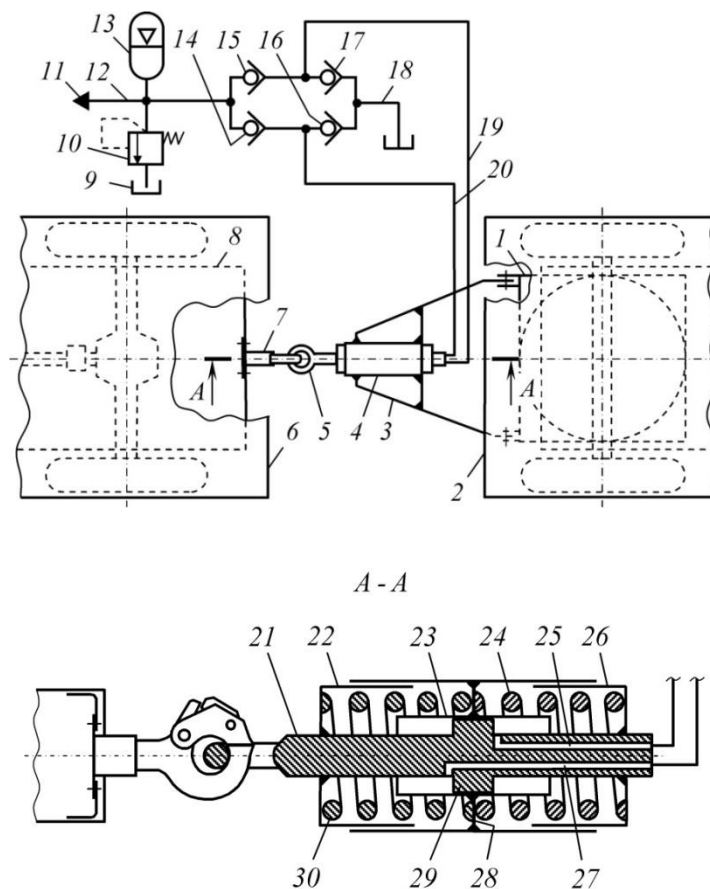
Схема предлагаемой конструкции рекуперативного ТСУ: 1 – поворотная рама передней колесной пары прицепа; 2 – прицеп; 3 – дышло; 4 – корпус рекуперативного механизма; 5 – соединительное кольцо; 6 – лесовозный автомобиль; 7 – крюк; 8 – рама; 9 – гидробак; 10 – предохранительный клапан; 11 – порт подключения к потребителю рекуперированной рабочей жидкости; 12 – всасывающий трубопровод; 13 – пневмогидравлический аккумулятор; 14–17 – обратные клапаны; 18 – напорный трубопровод; 19, 20 – гибкие трубопроводы; 21 – шток гидроцилиндра; 22, 26 – кожухи; 23 – гидроцилиндр; 24, 30 – пружины; 25, 27 – каналы; 28 – перегородка крепления гидроцилиндра; 29 – поршень
